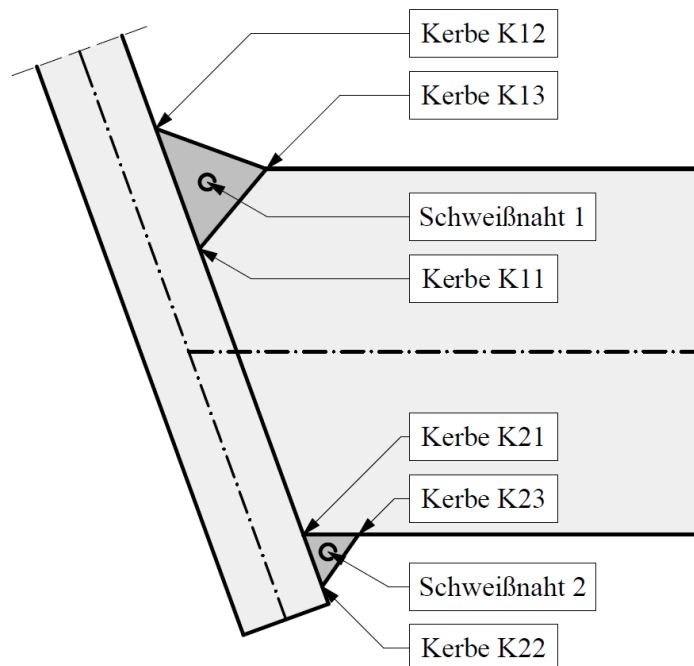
Definition der Schweißnähte und der kritischen Stellen K_{ij} .
